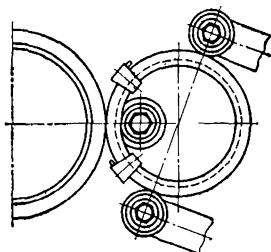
Схема полуоткрытого способа раскатки заготовок
